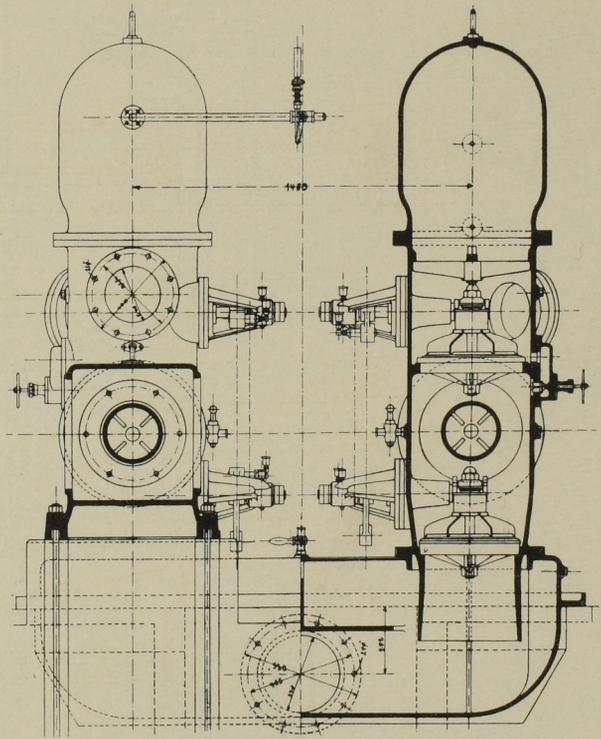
Grundriss der Pumpe. Masst. 1:30.
